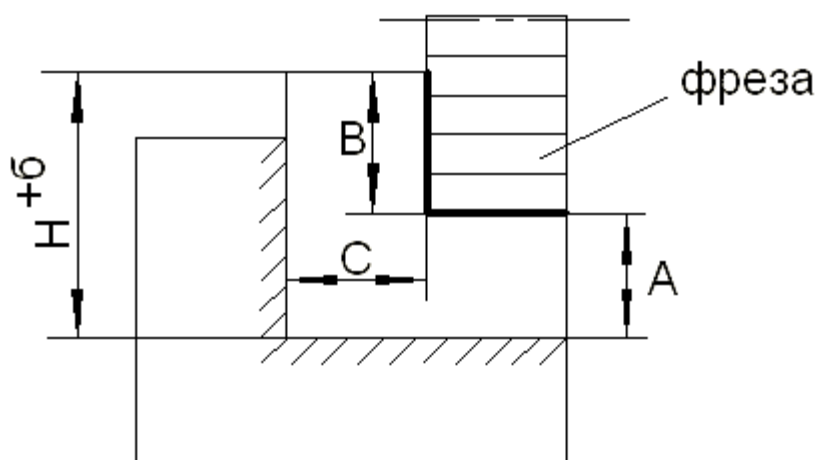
Схема базирования детали при фрезеровании уступа
